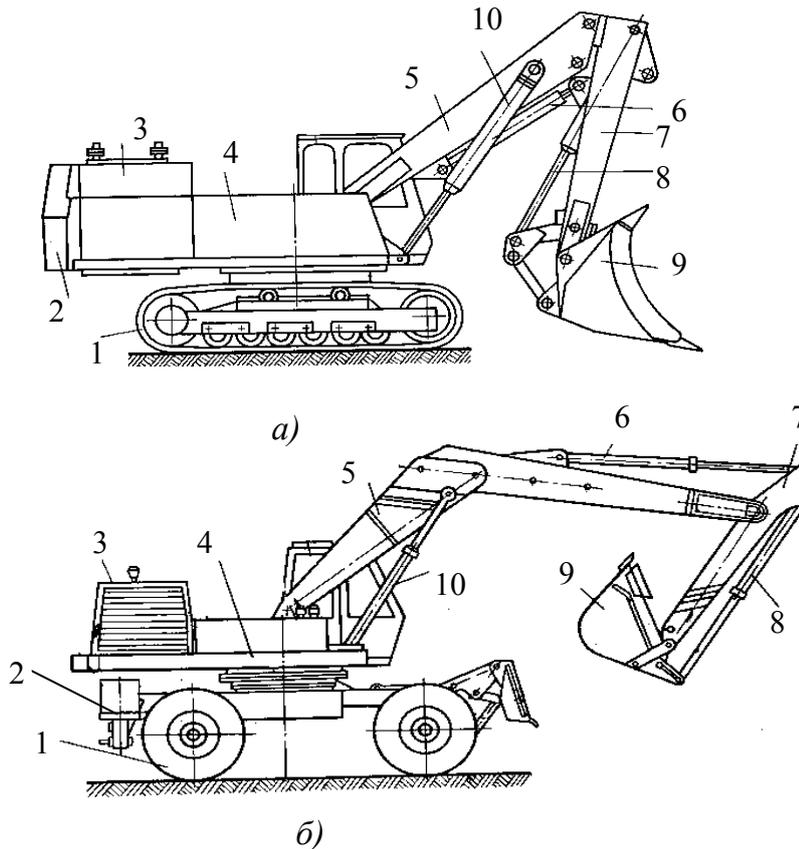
Одноковшовый гидравлический экскаватор: а – на гусеничном ходу (прямая лопата); б – на колесном ходу; 1 – ходовое оборудование; 2 – противовес; 3 – двигатель; 4 – поворотная платформа; 5 – стрела; 6 – гидроцилиндр управления; 7 – рукоять; 8 – гидроцилиндр управления ковшом; 9 – ковш; 10 – гидроцилиндр управления стрелой
